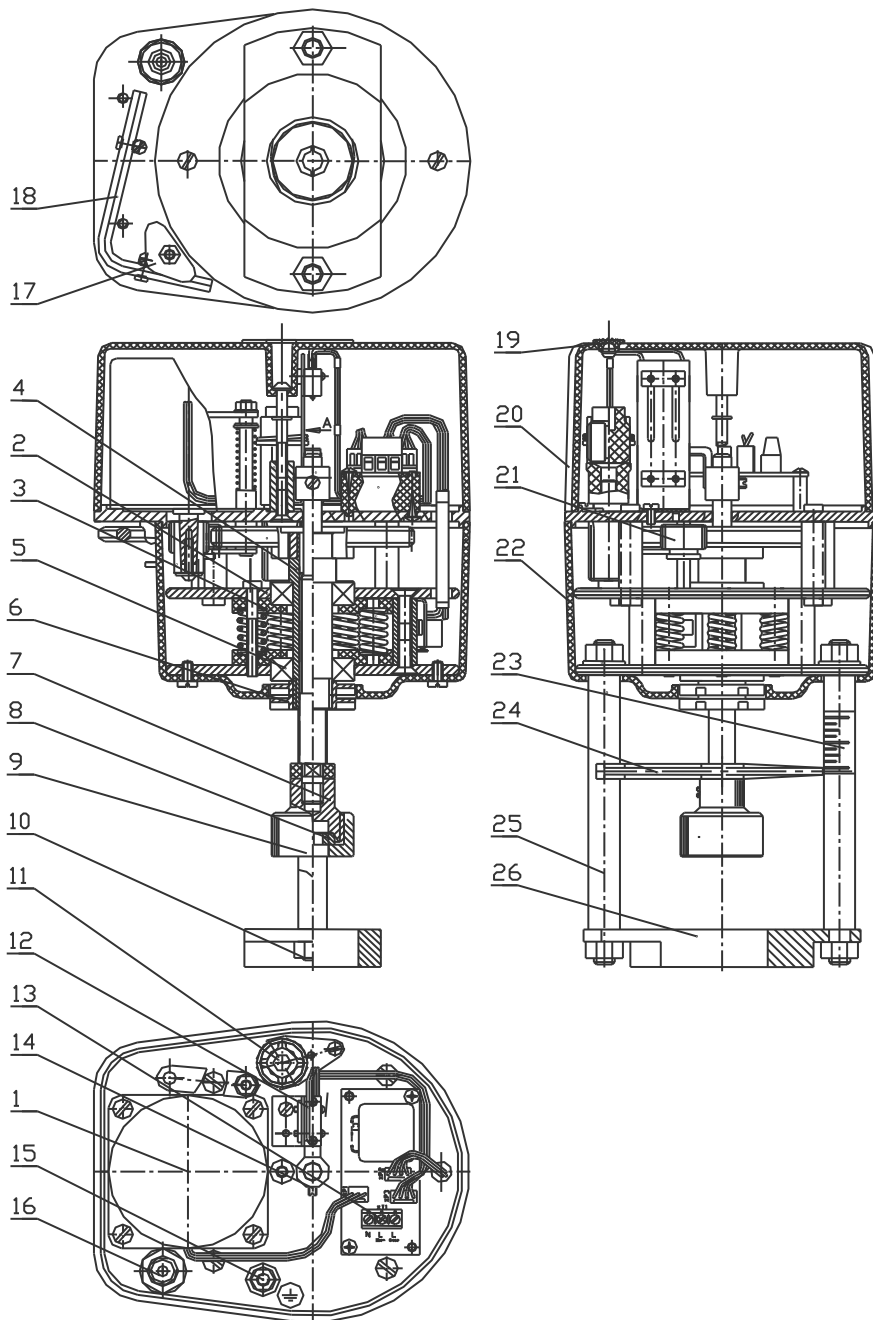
Устройство исполнительного механизма МЭП-1200/XX-20-В-Ф-57-35
